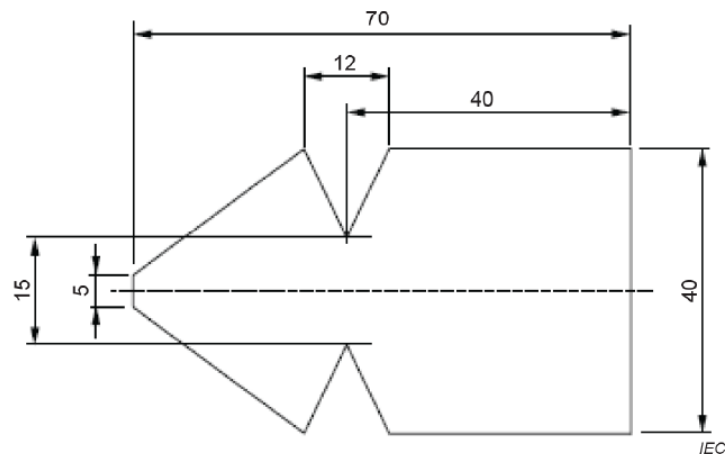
Dimensiones papel filtro (IEC 60587)
